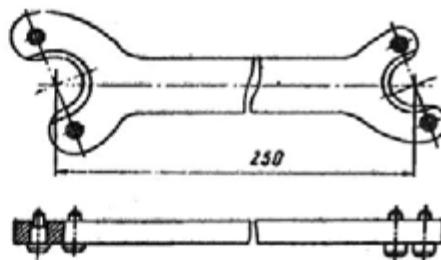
Ключ для отвертывания гайки резервуара амортизатора монтажный конец и с помощью торцового ключа отверните гайку 20 клапана отдачи (резьба правая).
